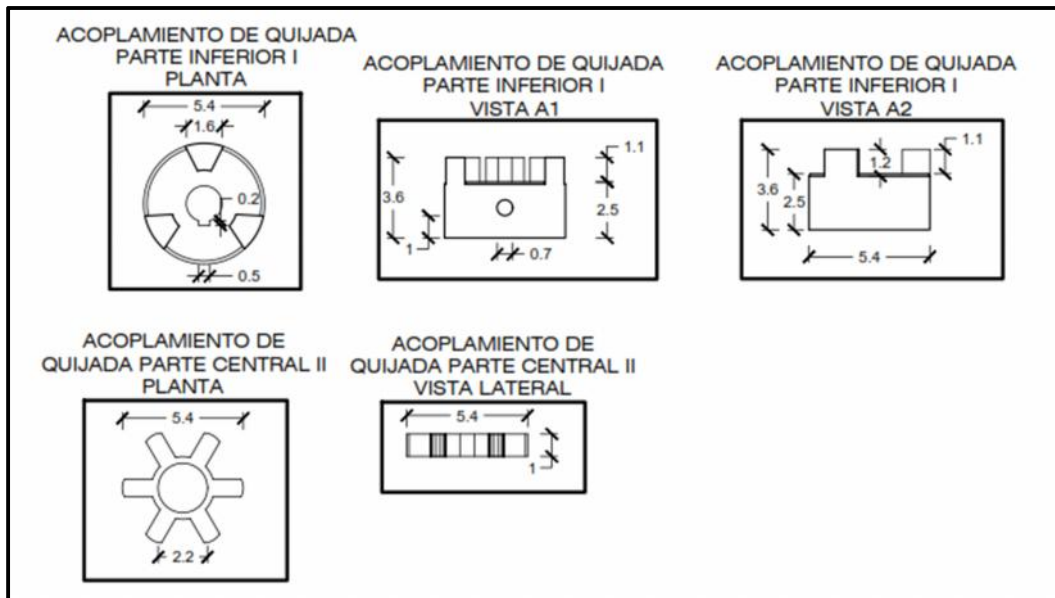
Vista lateral y planta del acoplamiento de quijada
